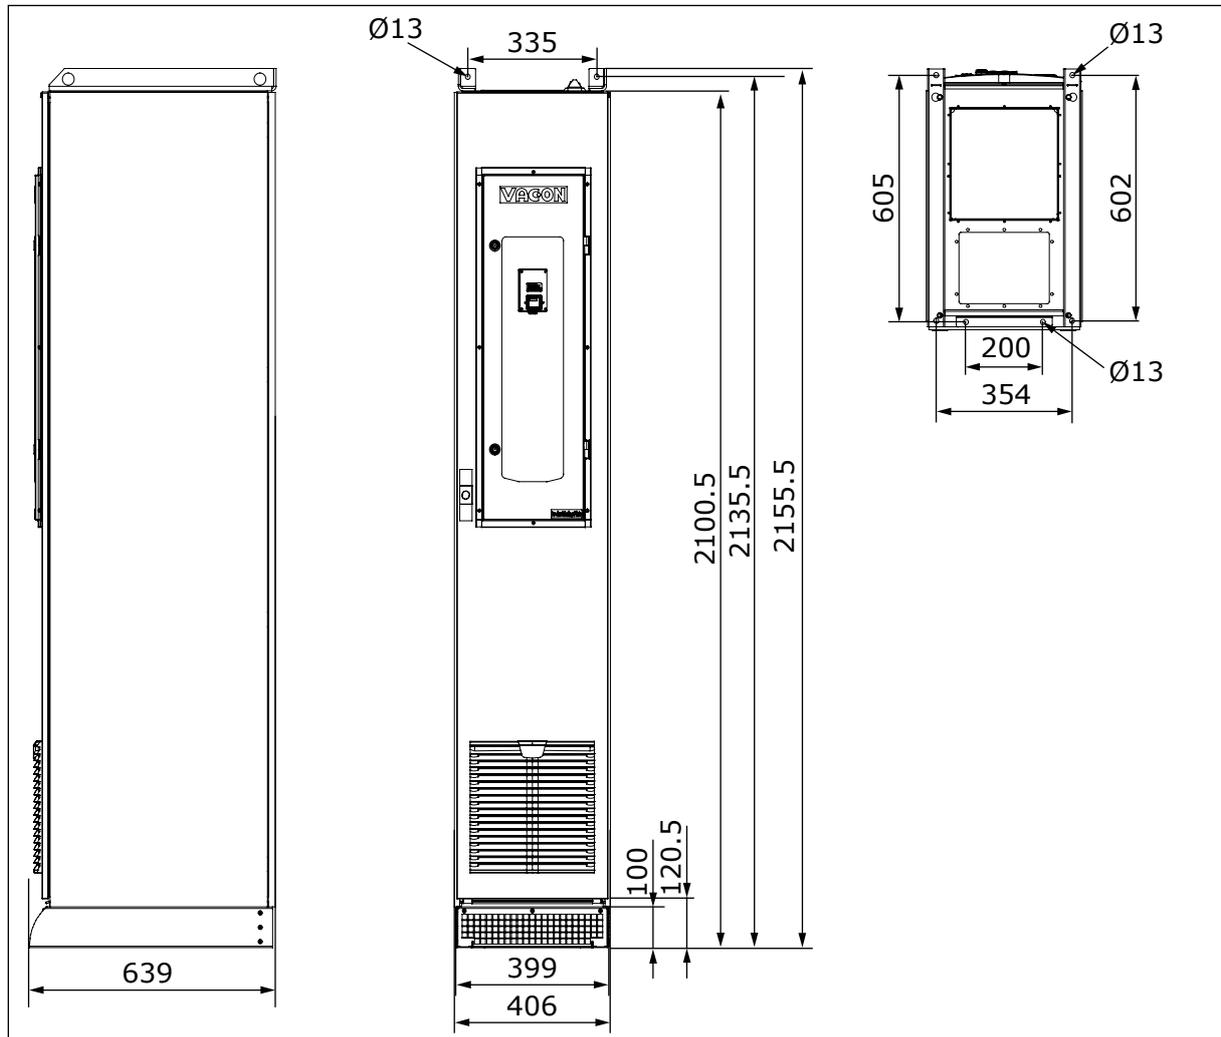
Abmessungen des Standard-Schaltschranks in mm, MR8, IEC
